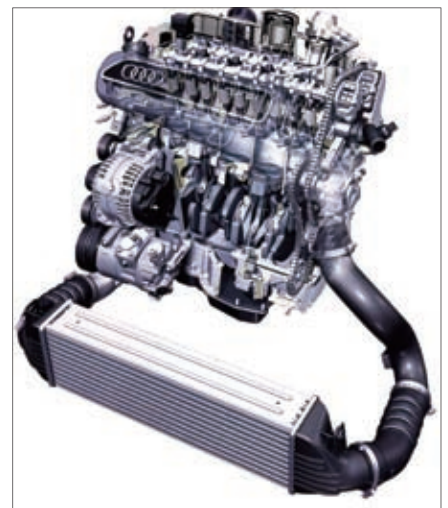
Audi-TT-RS轿车用5缸2.5L-TFSI直喷式汽油机剖视图
